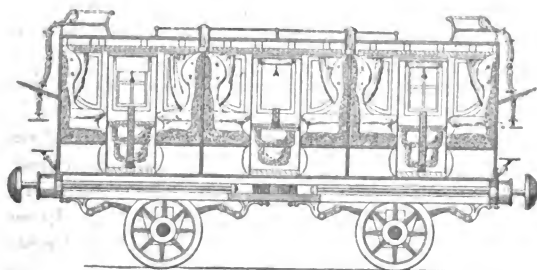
Coupe d'une voiture de 1<sup>re</sup> classe.
